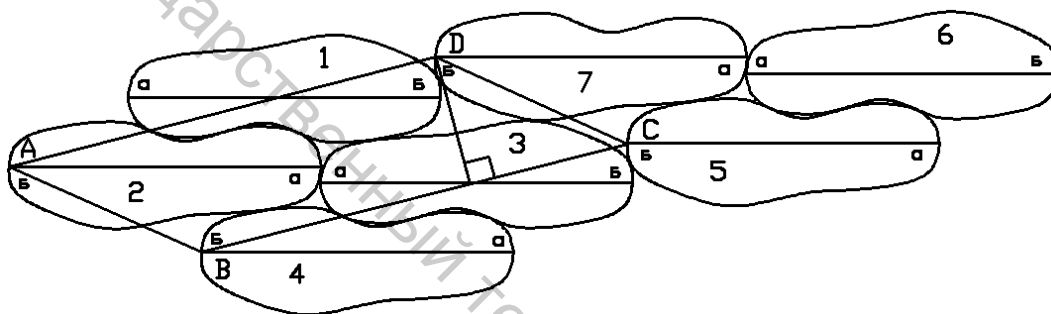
Схема совмещения подошв и стелек пяточными частями (вариант 2)
